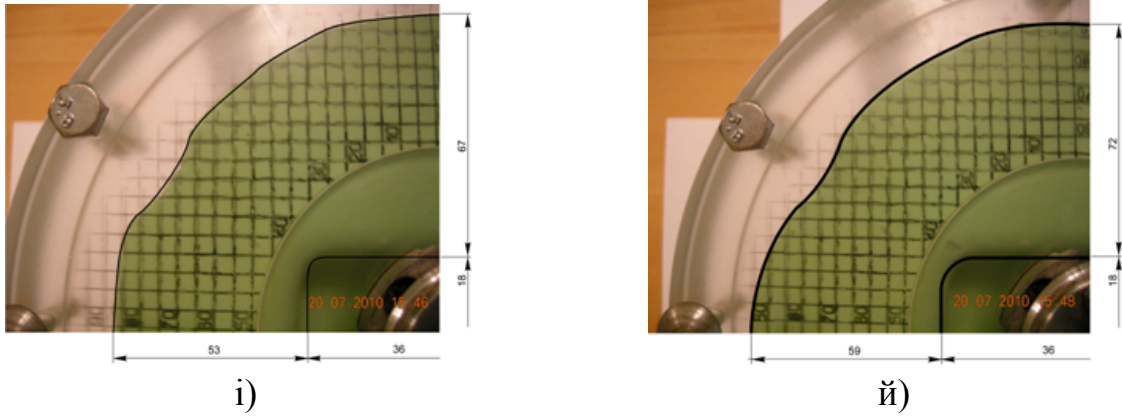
Результати “зворотного” витягування при різній глибині умовної коробчатої деталі прямокутної форми з розмірами у плані 72x36 мм.
